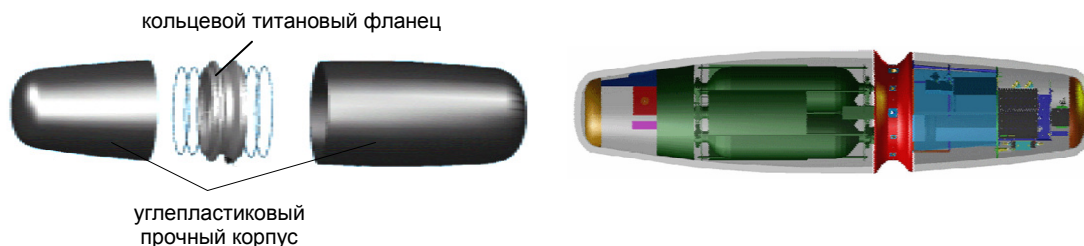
Конструкция прочного корпуса подводного аппарата ДеерС (соединение прочного корпуса с помощью титанового фланца) [79]
